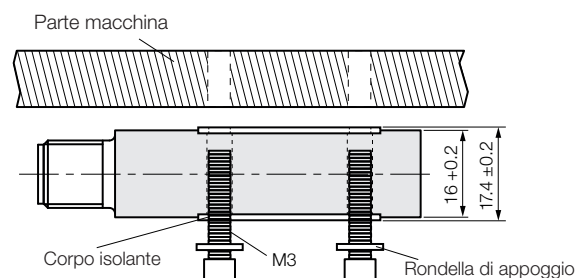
Montaggio della testa sensore con corpo isolante
